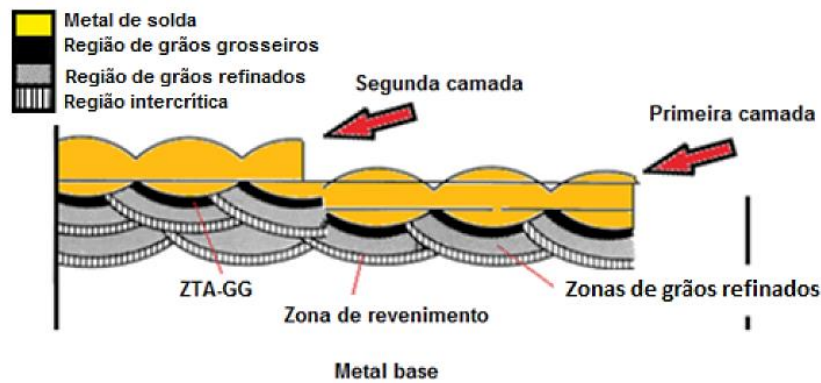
Diagrama esquemático de uma soldagem multipasses e o efeito do revenimento.
